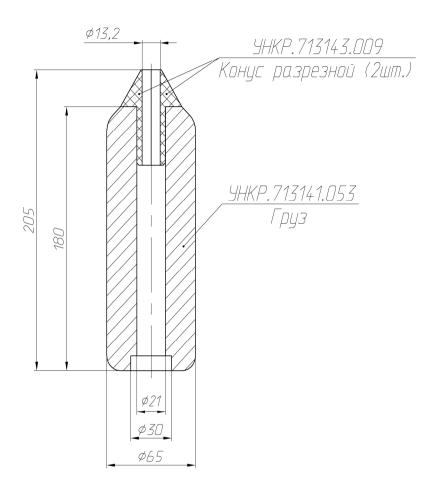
Габаритные размеры поплавка УНКР.305446.109
